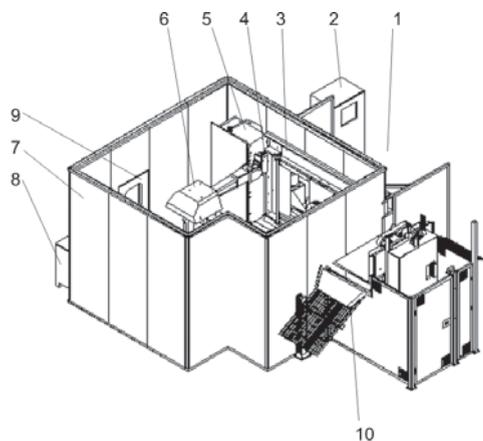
Схема обрабатывающего центра LCC фирмы Laempe: 1 – зона загрузки (вручную или вторым роботом); 2 – блок управления; 3 – поворотный портал; 4 – шпиндельный электропривод; 5 – магазин с инструментами; 6 – обрабатывающий робот; 7 – защитная кабина (шумоглушительного исполнения); 8 – блок управления роботом; 9 – двери обслуживания кабины; 10 – сортировщик металлоотходов (опцион)
